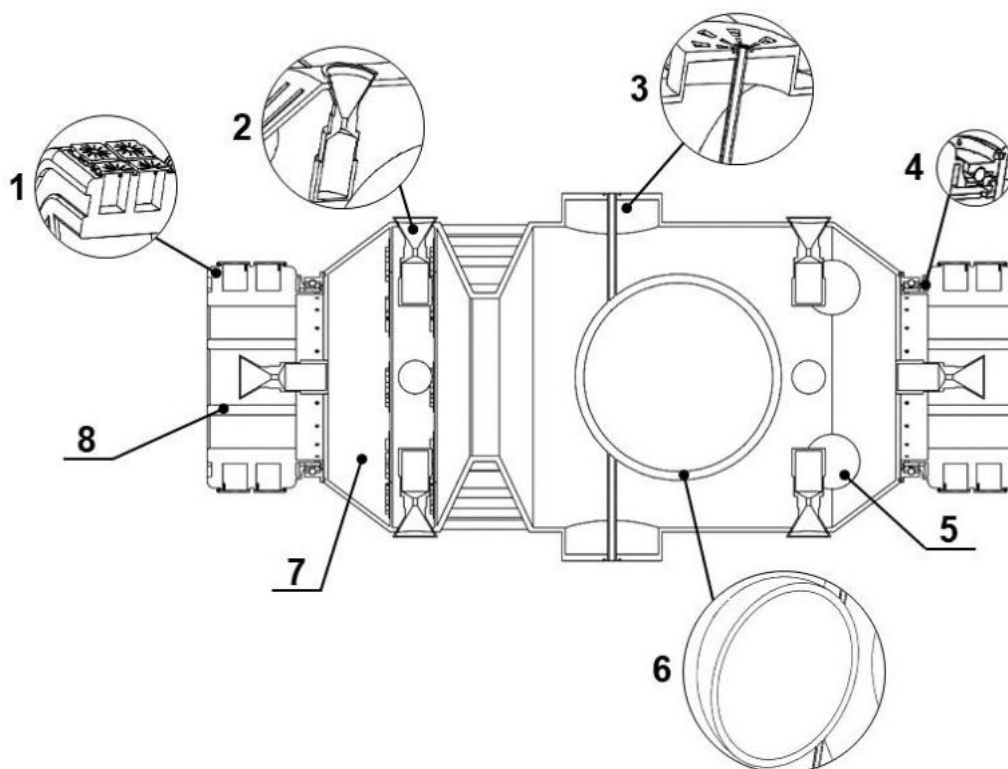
Заправочная станция в разрезе. 1 – пусковая камера с буксиром внутри; 2 – двигательная установка системы управления движением; 3 – специальный заправочный интерфейс; 4 – подшипниковый узел; 5 шар-баллон газа наддува; 7 – приборный отсек; 8 – пусковой модуль
